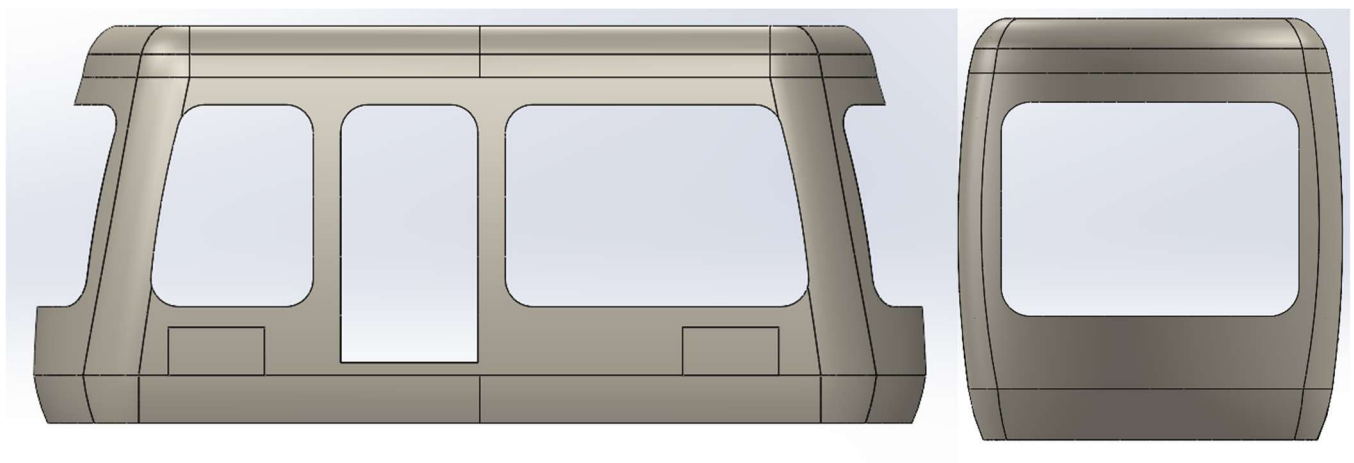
Alzado y vista lateral del diseño final de la estructura con los faldones y acabados.
